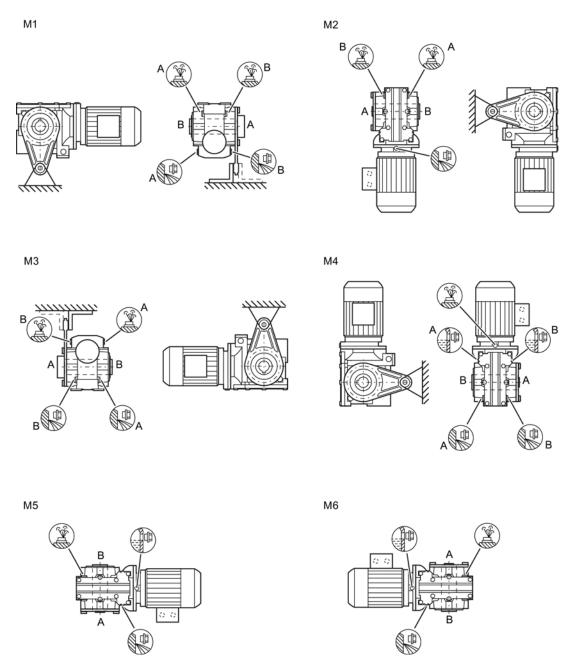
Posiciones de montaje para reductor helicoidal sinfín-corona CAD en versión enchufable, tamaño 29
